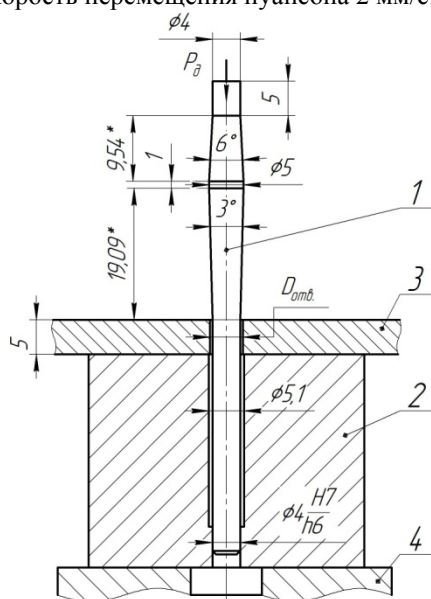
Схема процесса дорнования с размерами деформирующего инструмента (1 - дорн, 2 - матрица, 3 - заготовка, 4 - опора)
